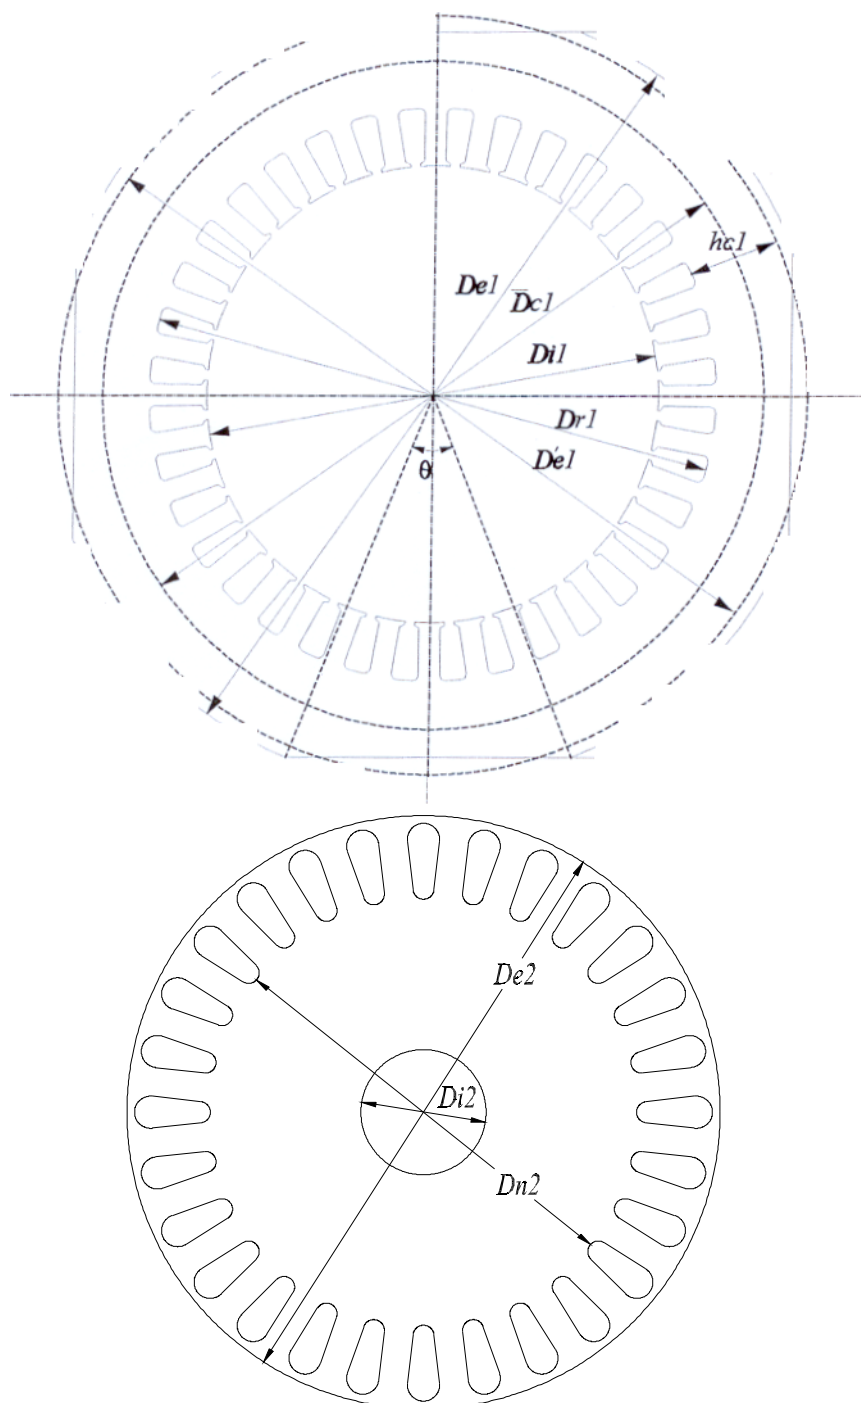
Dimensões do pacote de chapas do estator e do rotor
